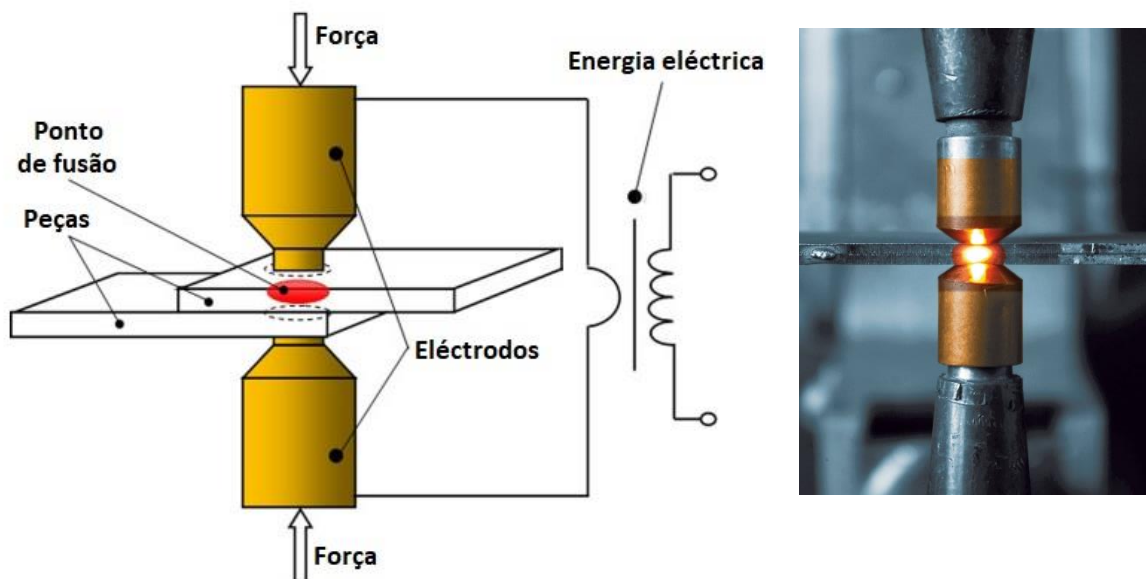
Soldadura de Pontos por Resistência (SPR) [Adaptado de (Luo, Rui, Xie, & Zhu, 2016) e (México)].
